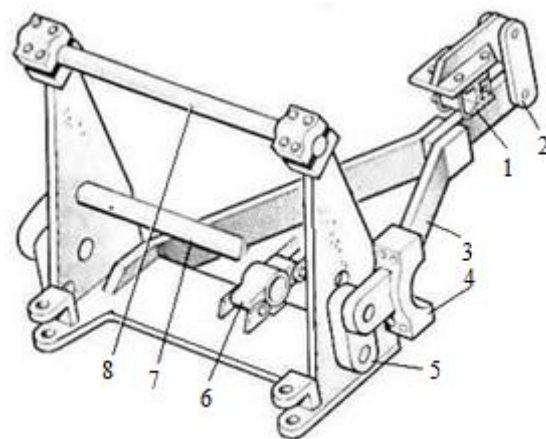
Переходная тензоплатформа для динамометрирования трактора с навесными орудиями: 1-рама; 2-подвеска; 3- тяга; 4-бугель; 5-подвеска; 6-тяговое звено; 7-нижний вал; 8-верхний вал
